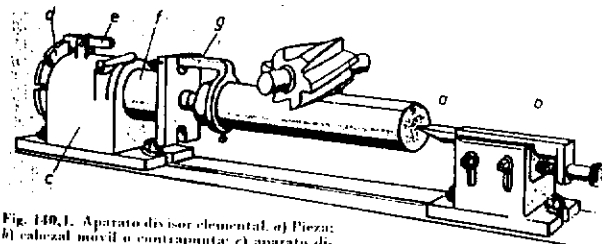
Aparato divisor elemental. a) Pieza; b) cabezal móvil o contrapunta; c) aparato divisor constituido por disco divisor d, trinquete e, husillo divisor f y pieza de anastre g.
